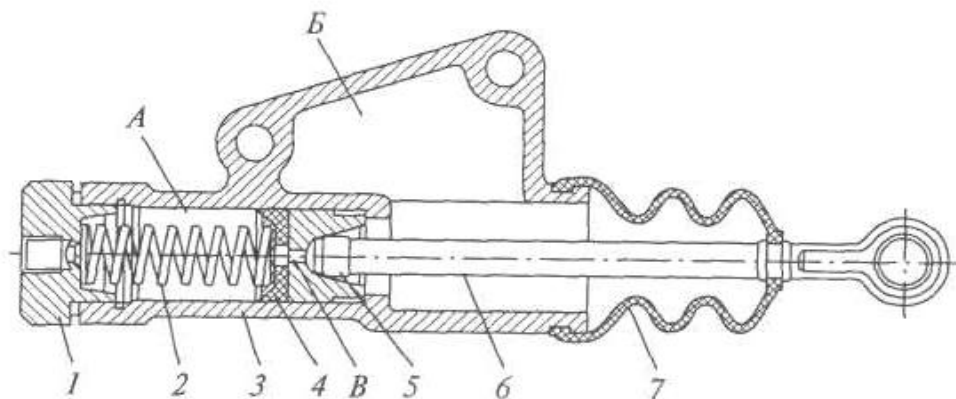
Главный цилиндр привода сцепления автомобиля КамАЗ:
